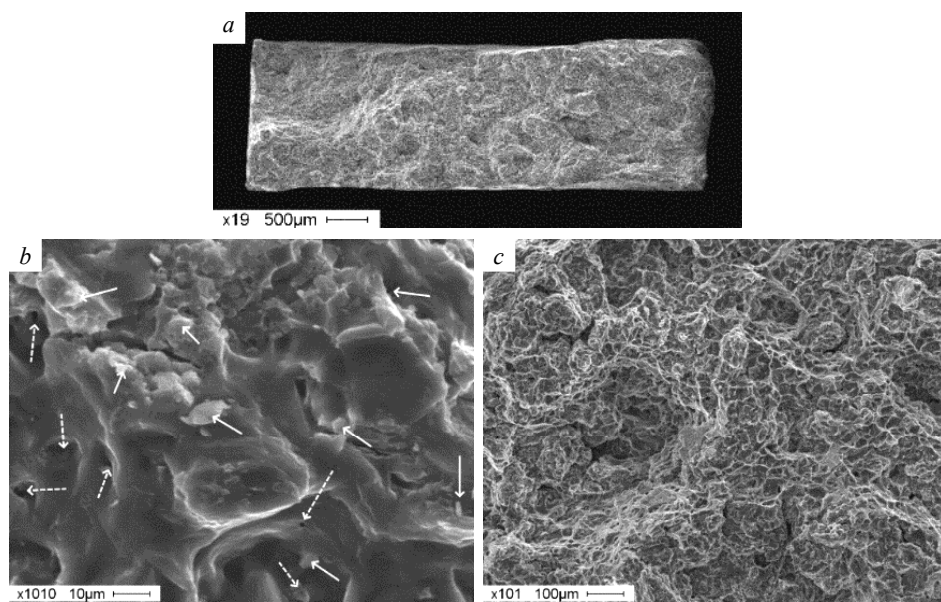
Поверхность излома образца из литого алюминиевого сплава группы 3 с добавлением частиц и с обработкой УЗ: *a* – общий вид поверхности разрушения, *b* – типичный вид излома; (*c*) отмеченные особенности разрушения
